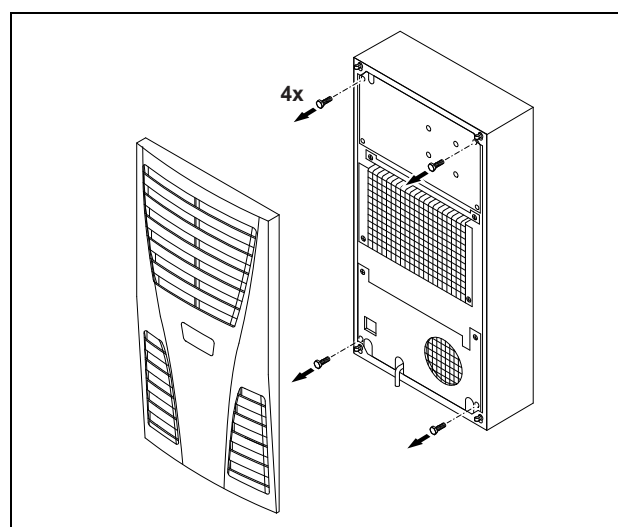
Připevnění chladicího zařízení (všechny typy kromě SK 3302.1xx)
